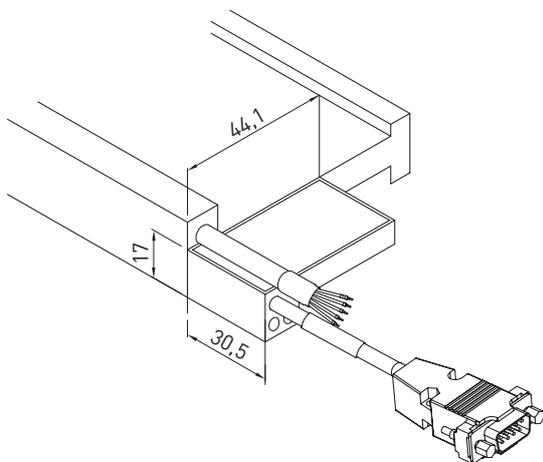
Beispielhafte Befestigung eines Hallensensors an einem LMC-Linearmotor
